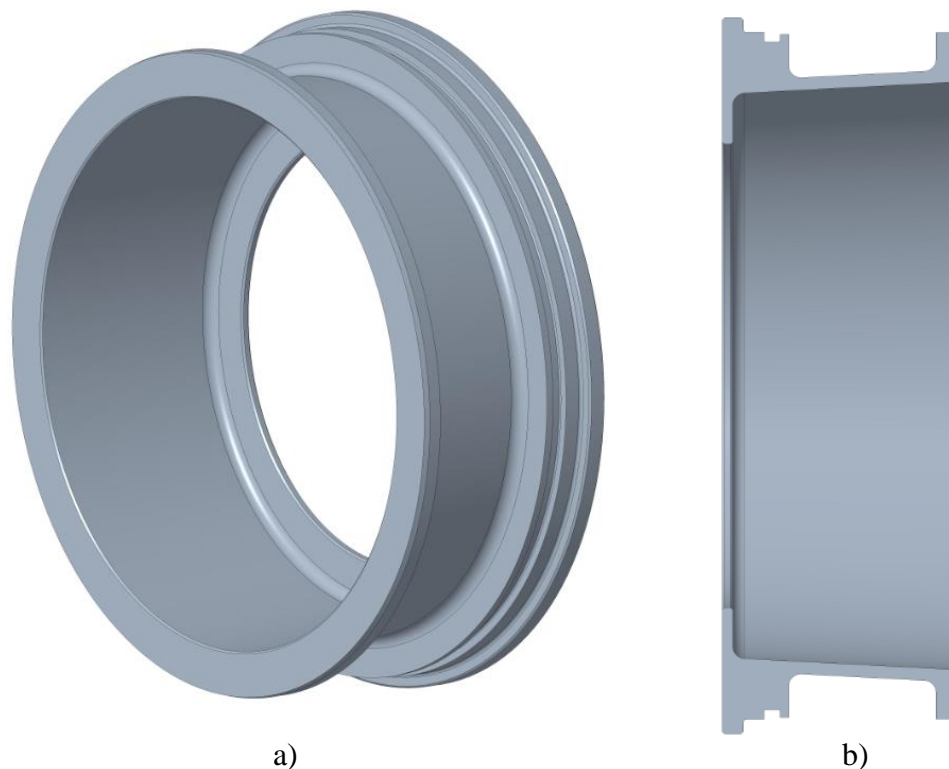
Model dorazového kroužku: a) obecný pohled, b) zobrazení v řezu
